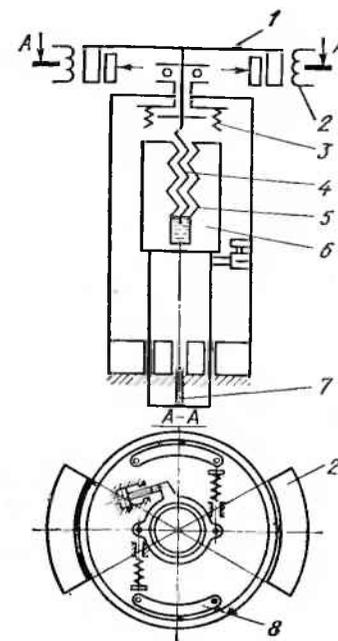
Схема винтового пресса с дугостаторным приводом:
